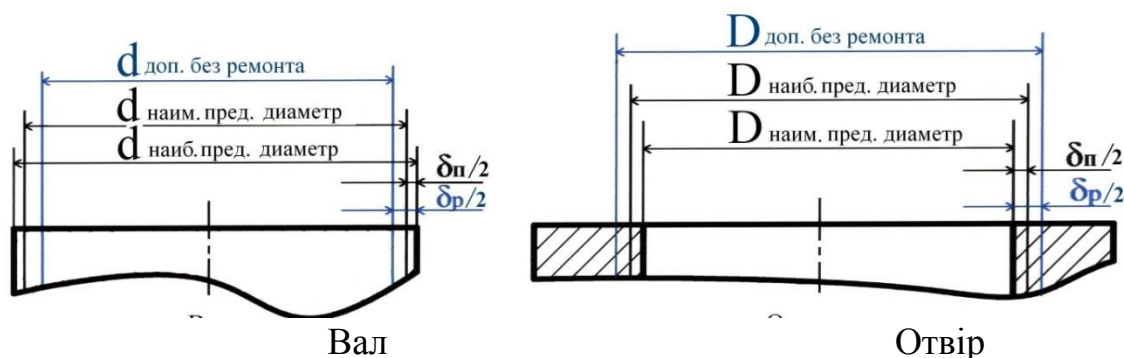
Ремонтні і виробничі допуски робочих поверхонь деталей.
